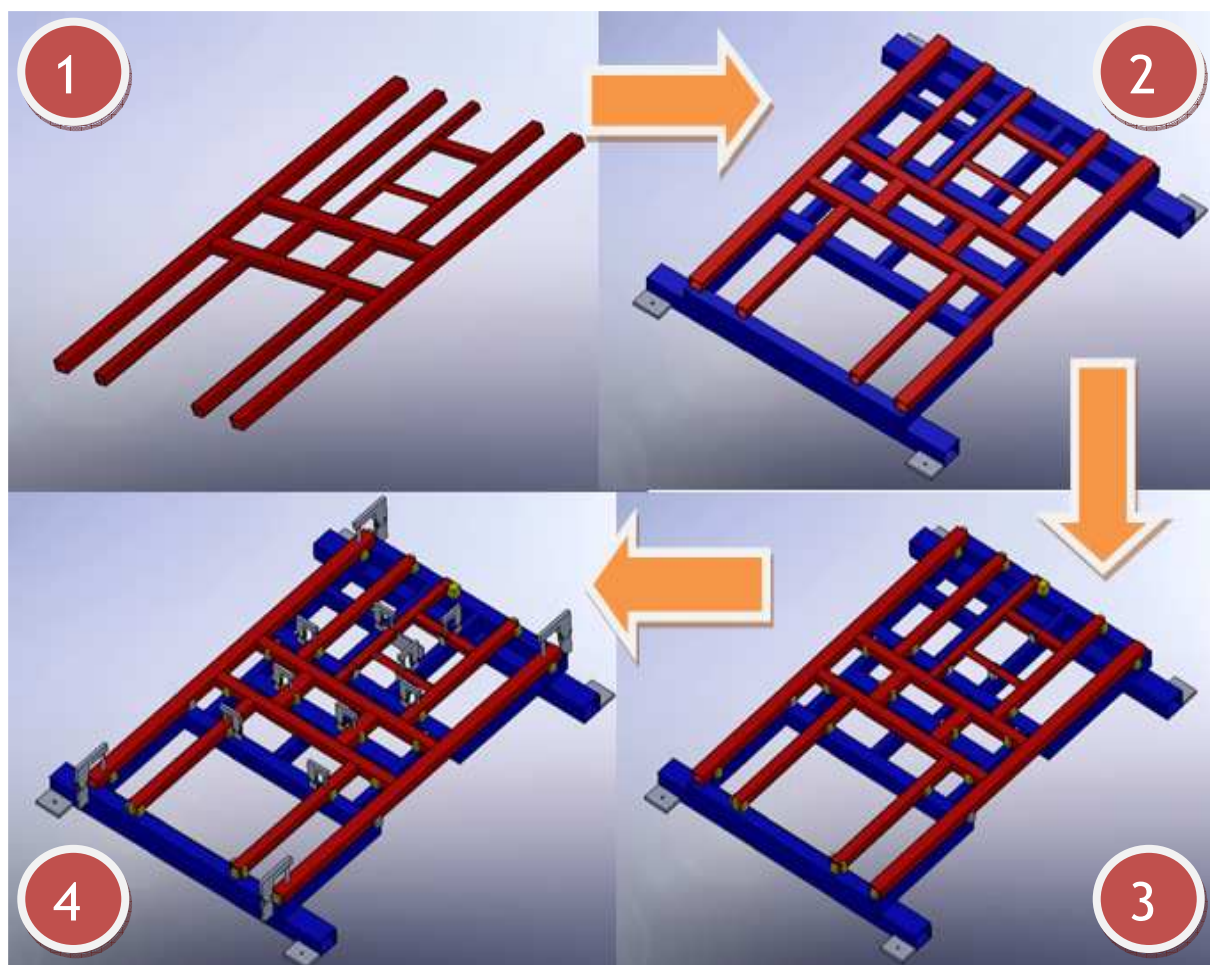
IMAGEM ILUSTRATIVA DAS ÉTAPAS DE MODELAÇÃO EFECTUADAS EM SOLIDWORKS DA PEÇA E GABARITO DE SOLDADURA
